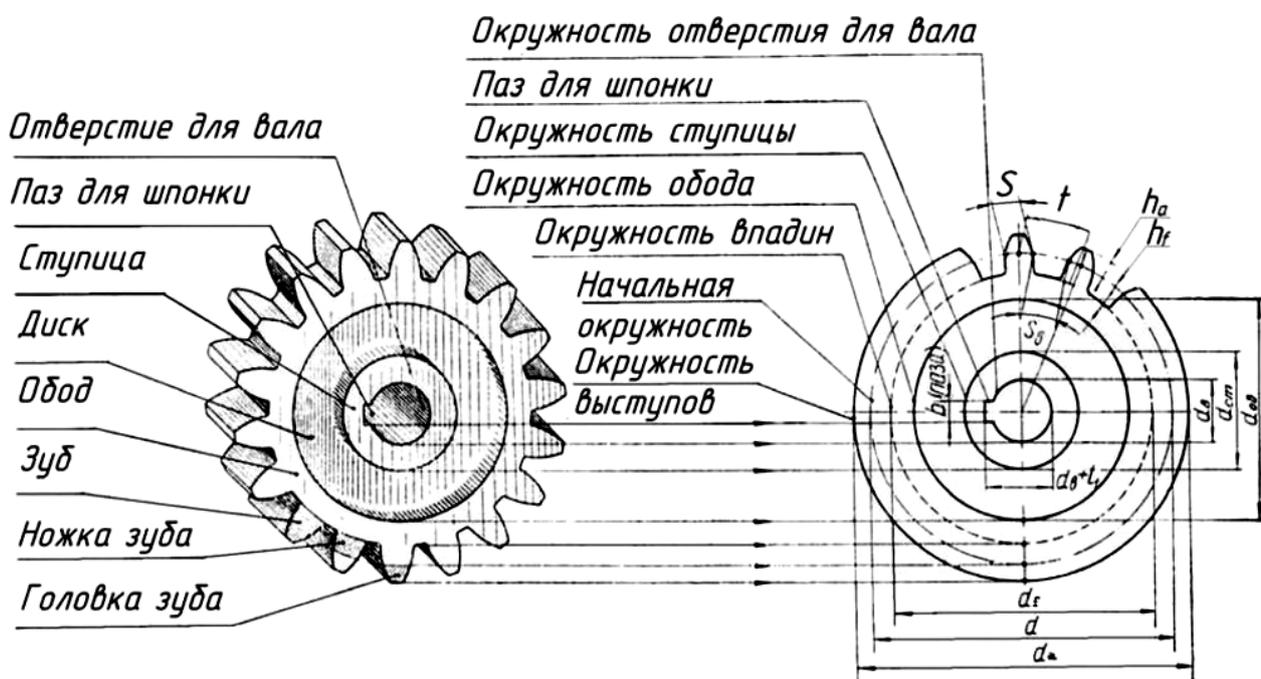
Основные параметры цилиндрического зубчатого колеса
